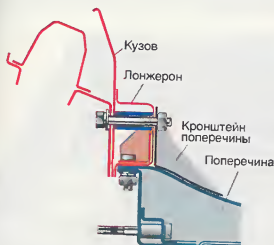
Схема крепления поперечной балки подвески к лонжерону.
